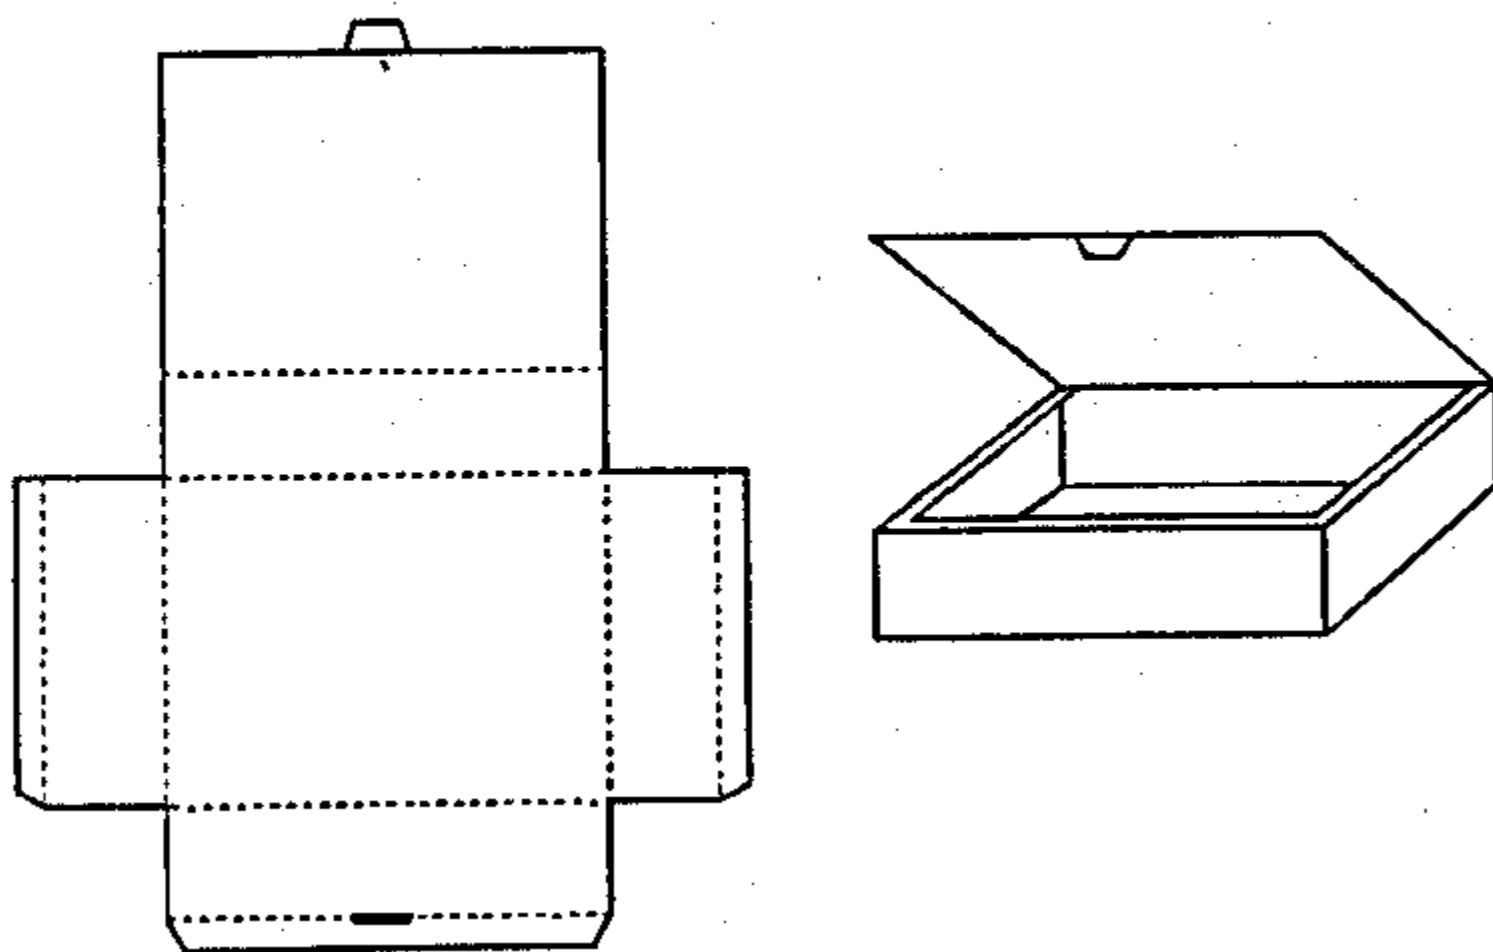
Изготовление коробки для коллекции сухих раковин моллюсков
